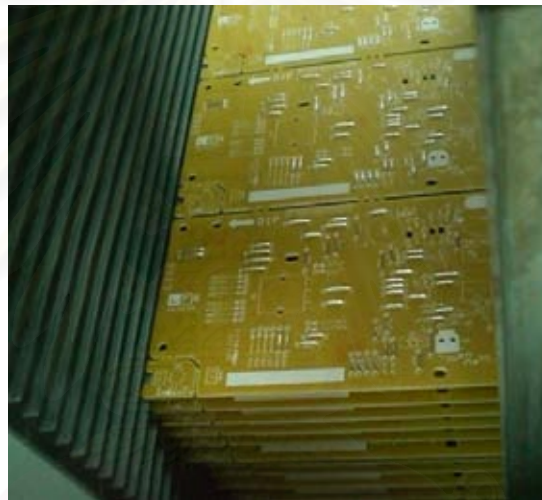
ส่วนของ Loader Board Feeder
